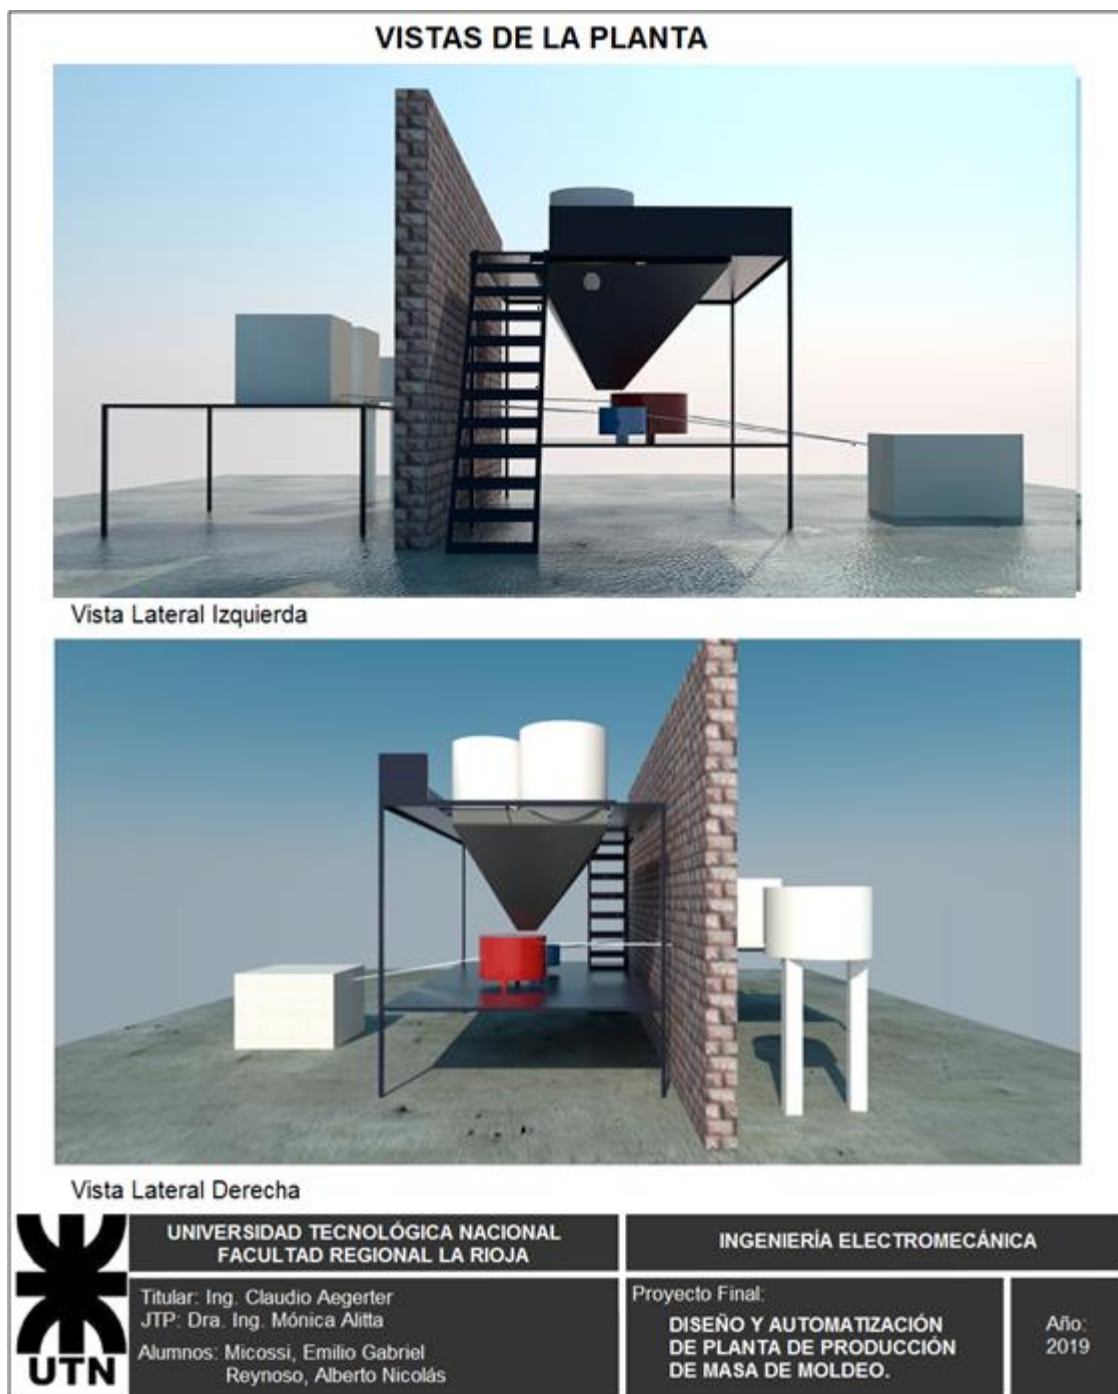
Plano de la planta con las vistas lateral derecha y lateral izquierda.
